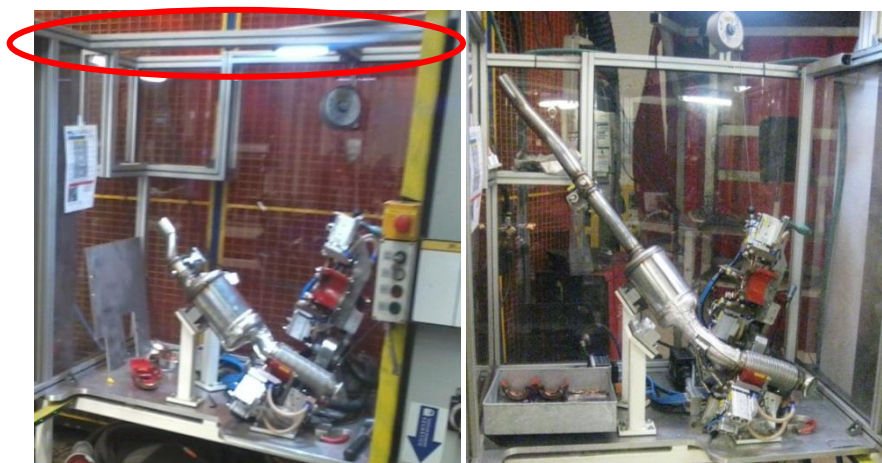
Máquina de soldadura con larguero y sin larguero
